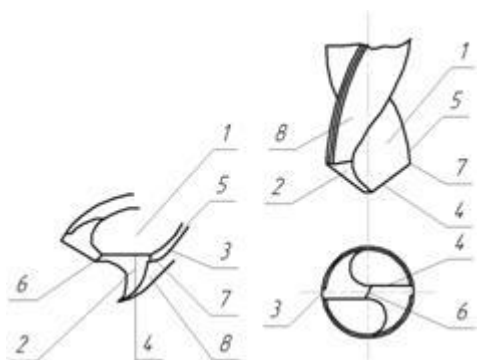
Поверхности лезвий сверла и его режущие кромки
